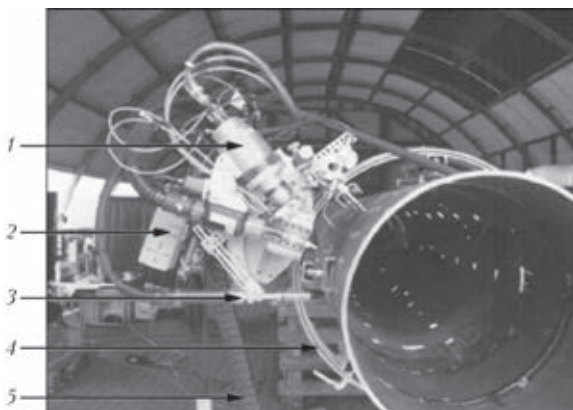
Сварочный комплекс для гибридной лазерной сварки: 1 — головка для гибридной сварки; 2 — перемещающийся трактор с датчиком управления; 3 — горелка в положении заполнения разделки; 4 — кольцо; 5 — шланг
